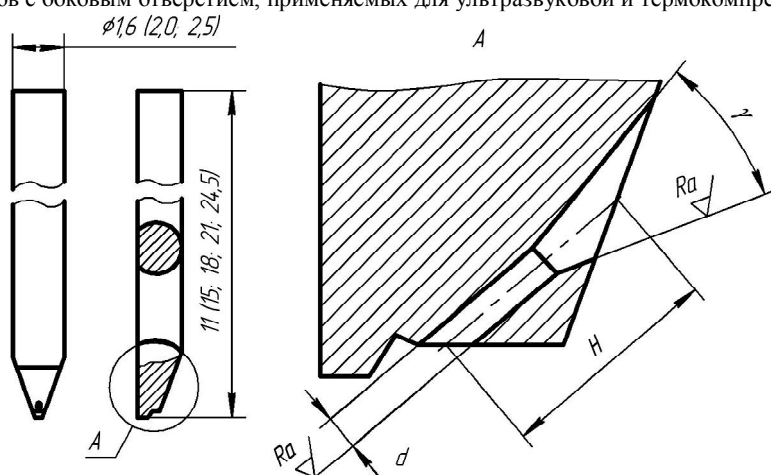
Инструмент для микросварки с боковым отверстием типа КУТ-1
